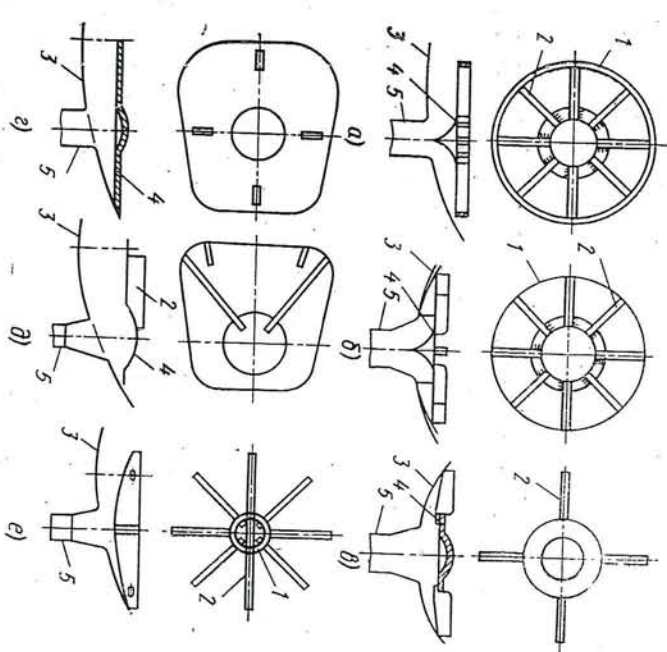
Принципиальные схемы конструкций воронкообразных устройств: а, б — радиальные ребра, устанавливаемые над тарелкой; в — тарелка неправильной формы; г — радиальные ребра; 1 — концентрическое ребро; 2 — радиальное ребро; 3 — днище бака; 4 — тарелка воронкообразная; 5 — слив
